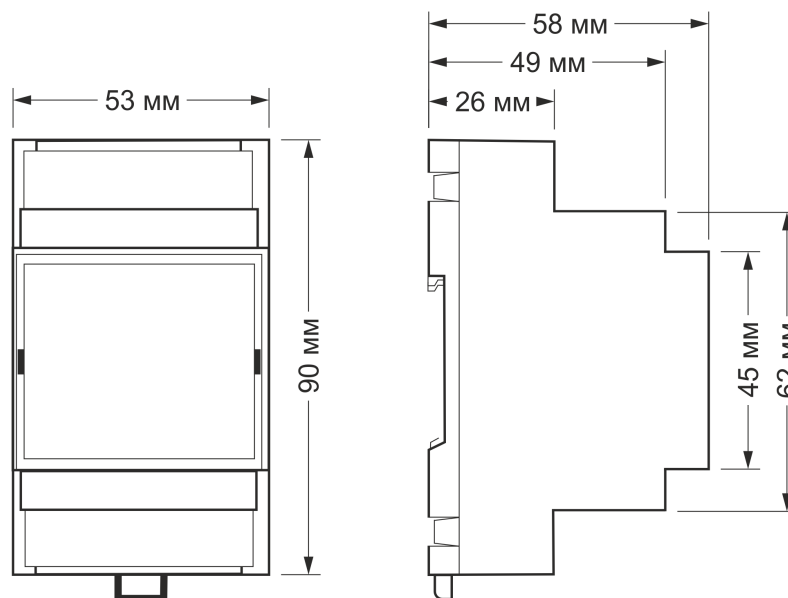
Габаритные размеры WB-MR6C в корпусе 3 DIN
